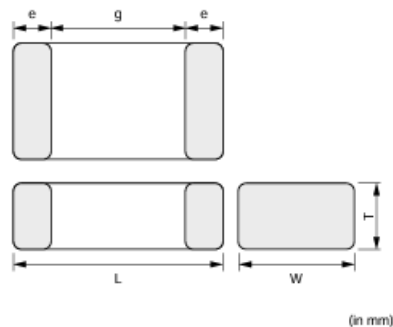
Зовнішній вигляд і розміри корпусу керамічного резонатора CSTCE8M00G55-R0
